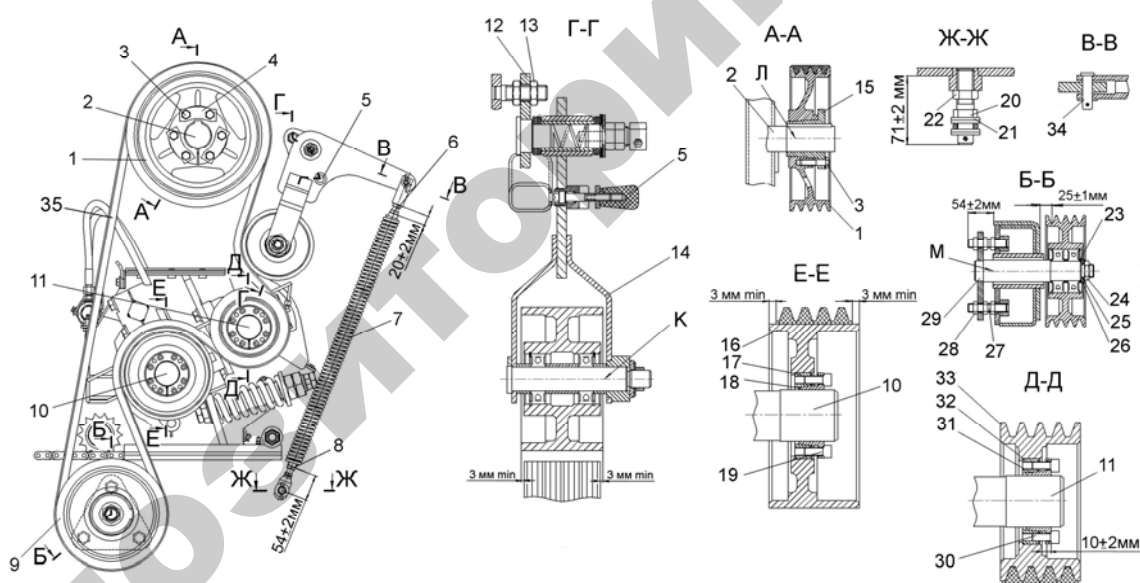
Регулировка привода доизмельчающего устройства:
